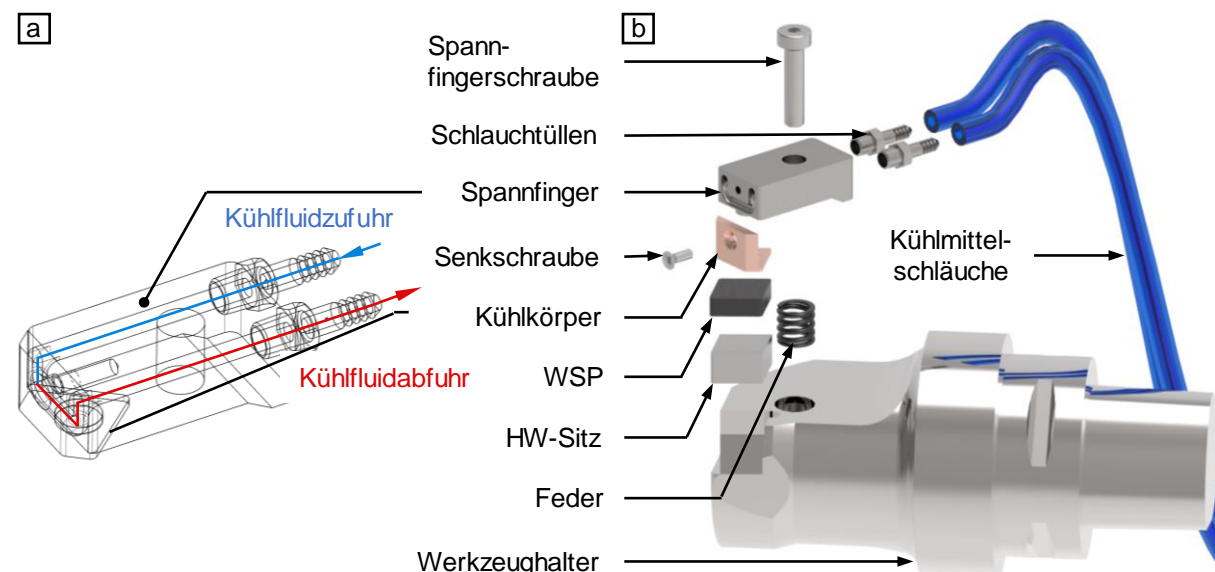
Dritter Vorentwurf; a) Schnittansicht; b) Explosionsansicht
